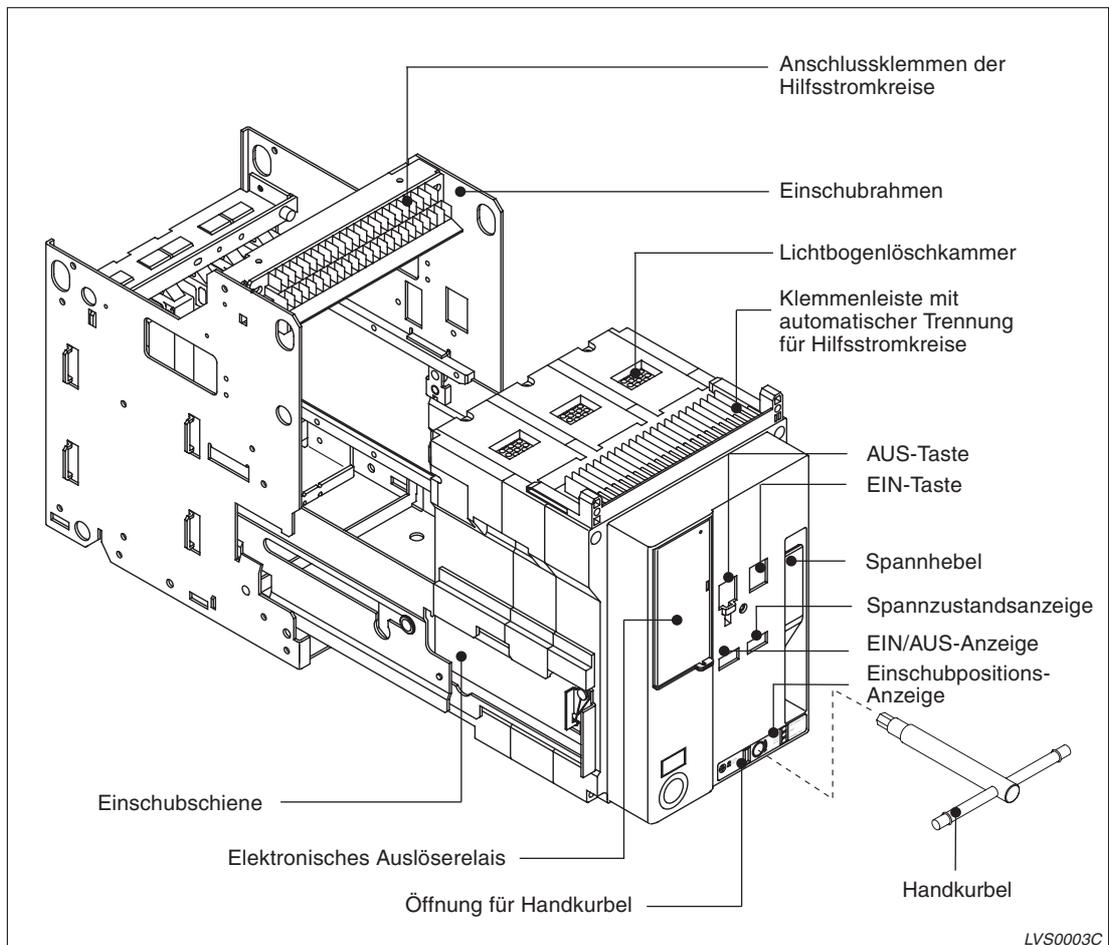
Vorderansicht Einschubtyp (ausgeschoben)
